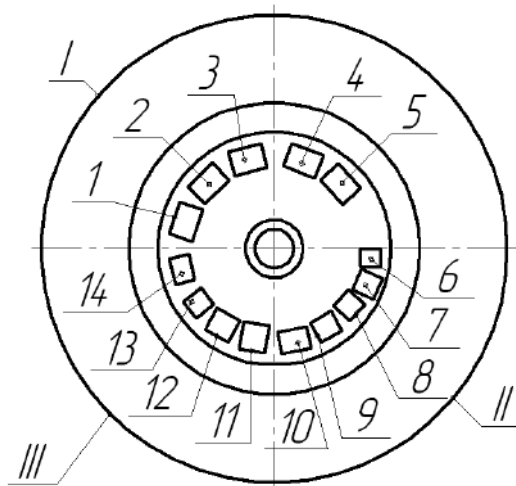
Знаки маркировки и клейма на правом торце оси колесной пары с подшипниками скольжения и качения без торцового крепления гайкой
